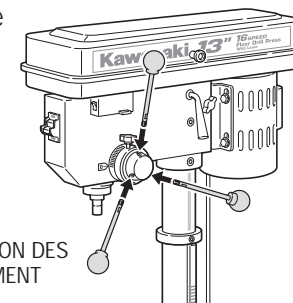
INSTALLATION DES LEVIERS D'AVANCEMENT
